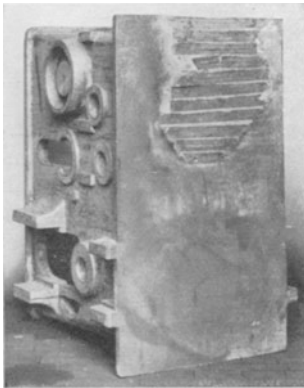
Warmschweißung eines Pressentisches.
